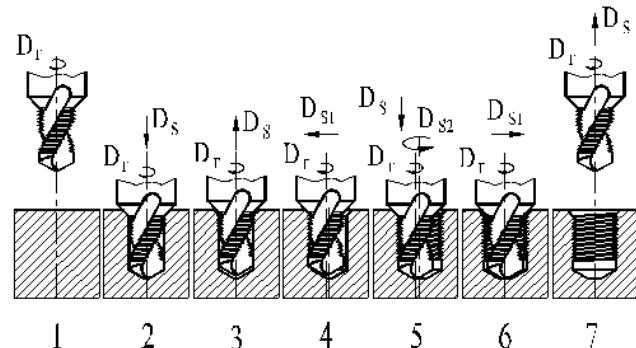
Типовая технологическая последовательность обработки ОСП сверло-резьбофрезой
